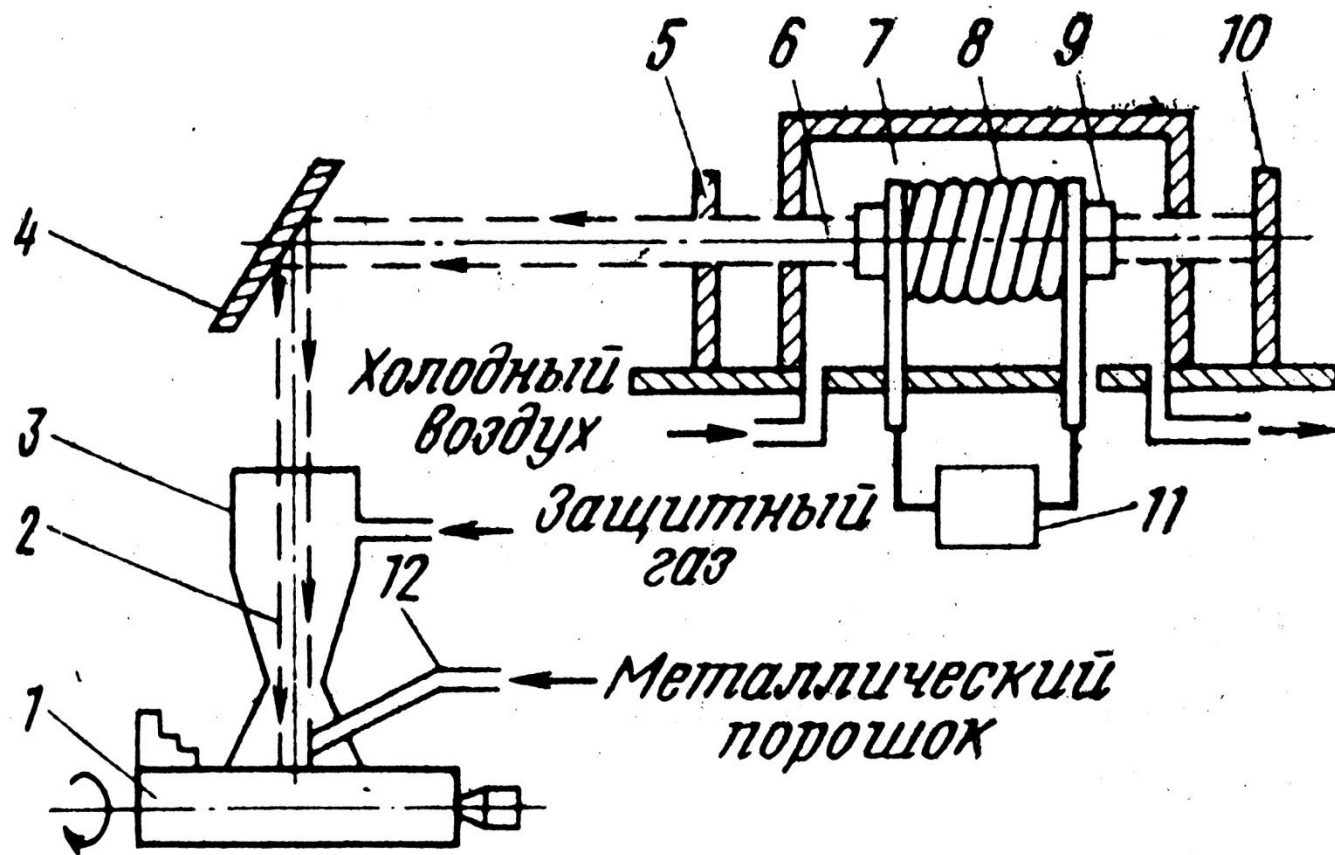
Схема установки для лазерной сварки и наплавки с рубиновым генератором
